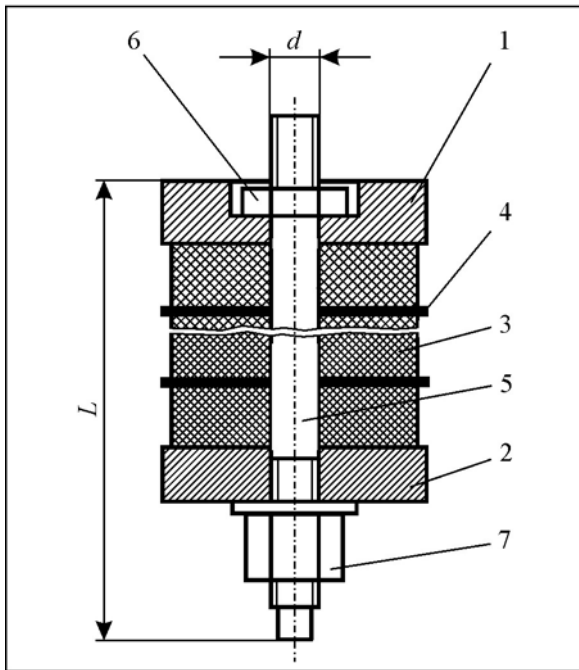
Стандартний буфер з гумовими пружинами: 1 – верхня шайба; 2 – нижня шайба; 3 – гумова пружина; 4 – прокладка; 5 – шток; 6 – гайка
